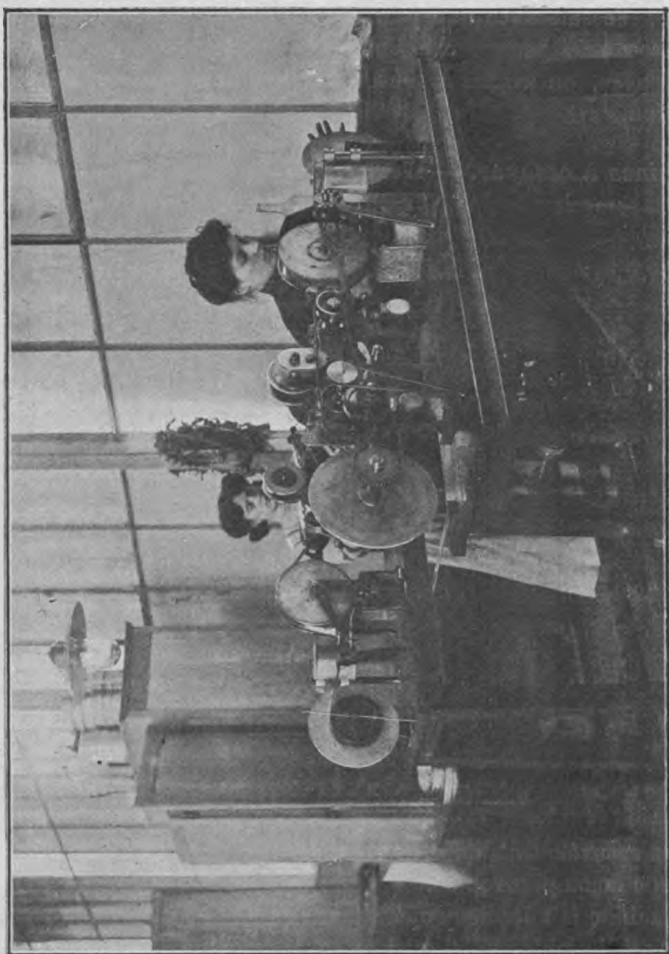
Machines à essuyer les films à l'usine « Lux ».
